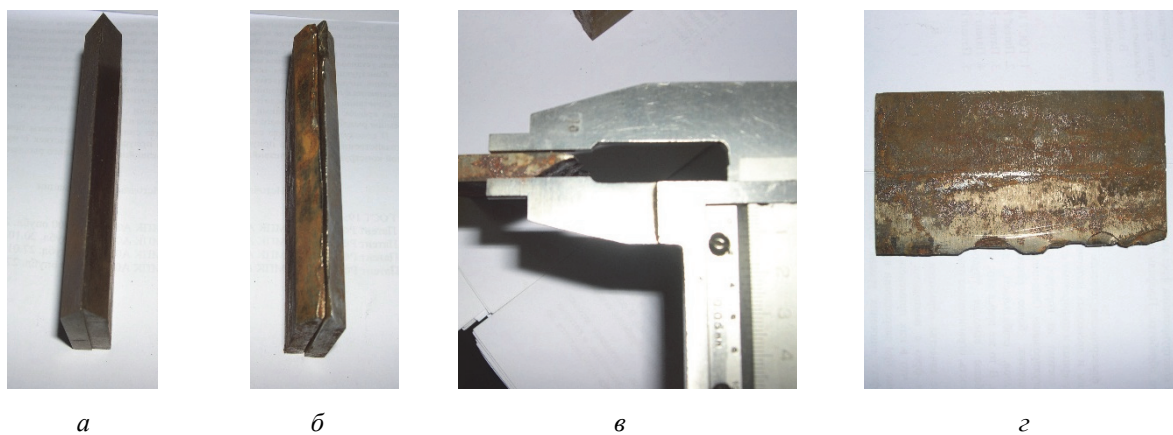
Вид разрушения рубильных ножей из биметаллических заготовок (сталь 35 и 9ХФ):
